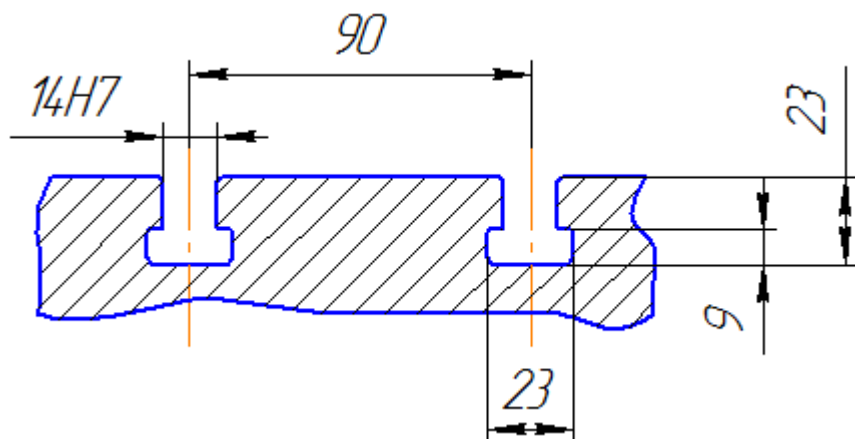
Посадочні і приєднувальні бази стола фрезерно- координатного верстата HAAS VM-3
